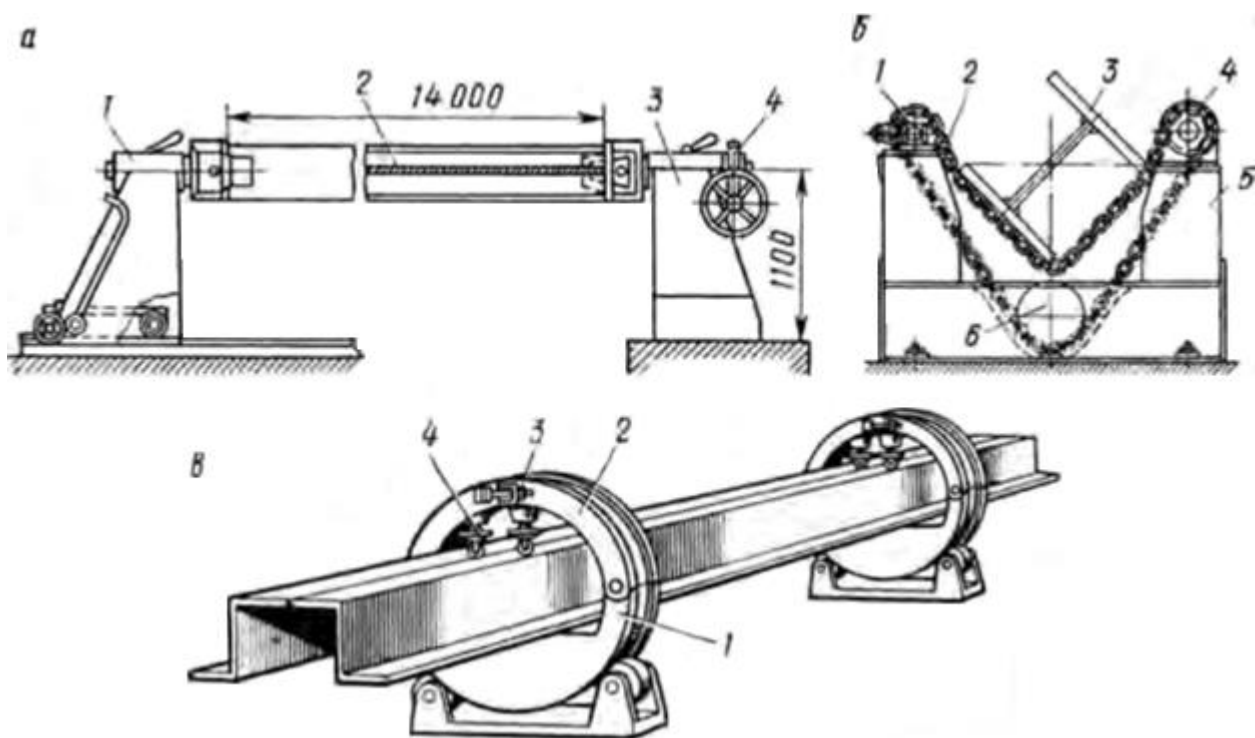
Схемы позиционеров-кантователей для сварки балок:
